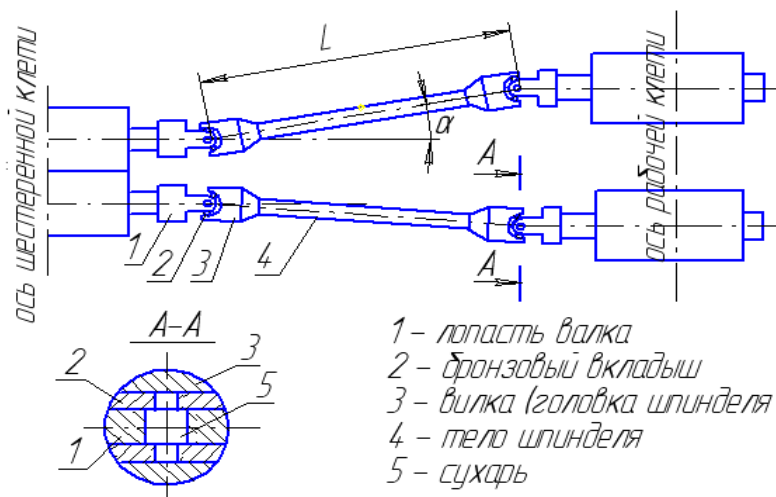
Схема установки универсальных шпинделей и конструктивные элементы шарниров
